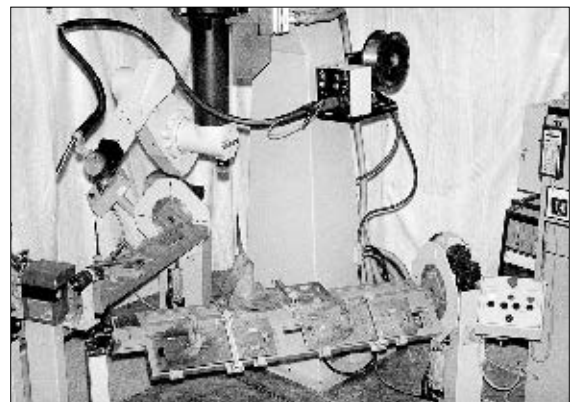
РТК дуговой сварки контрольного узла стрелочного перевода
